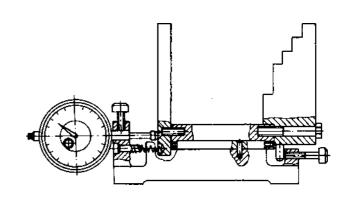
Приспособление для установки резца на шпиндель ϕ 78 мм
